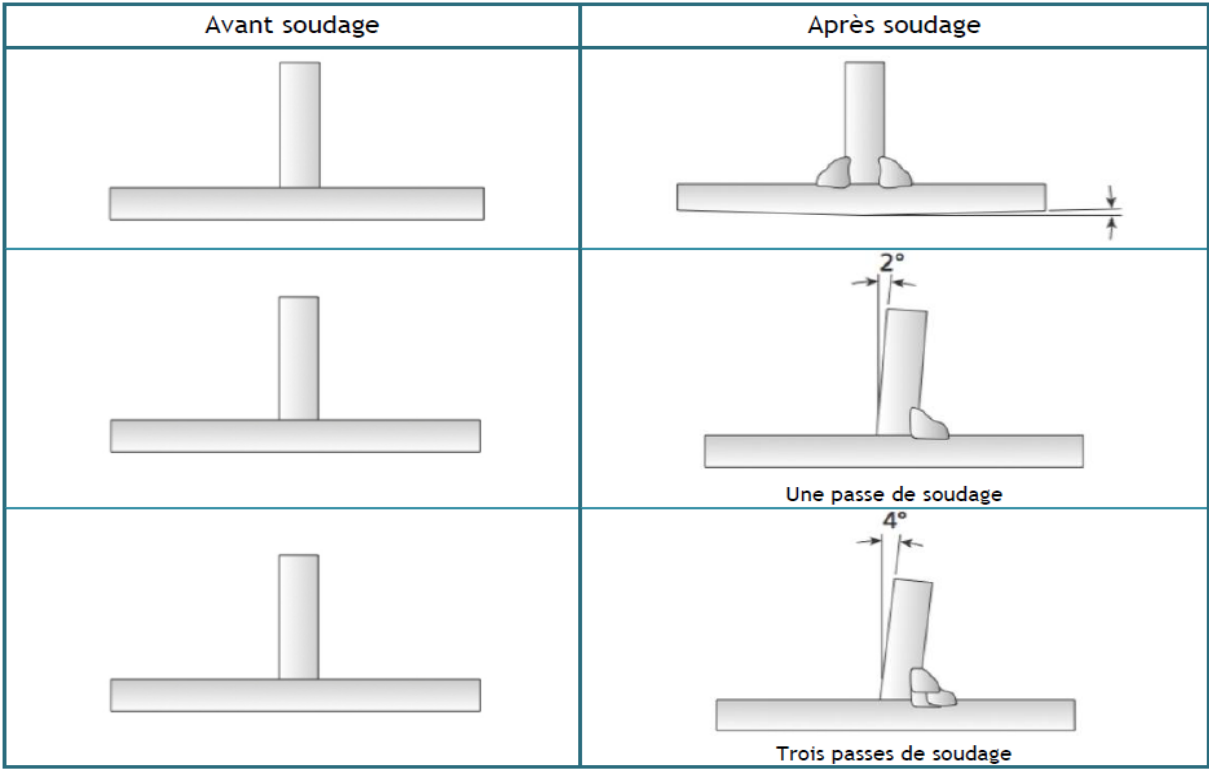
Déformations de soudage d'assemblages en T [12]
